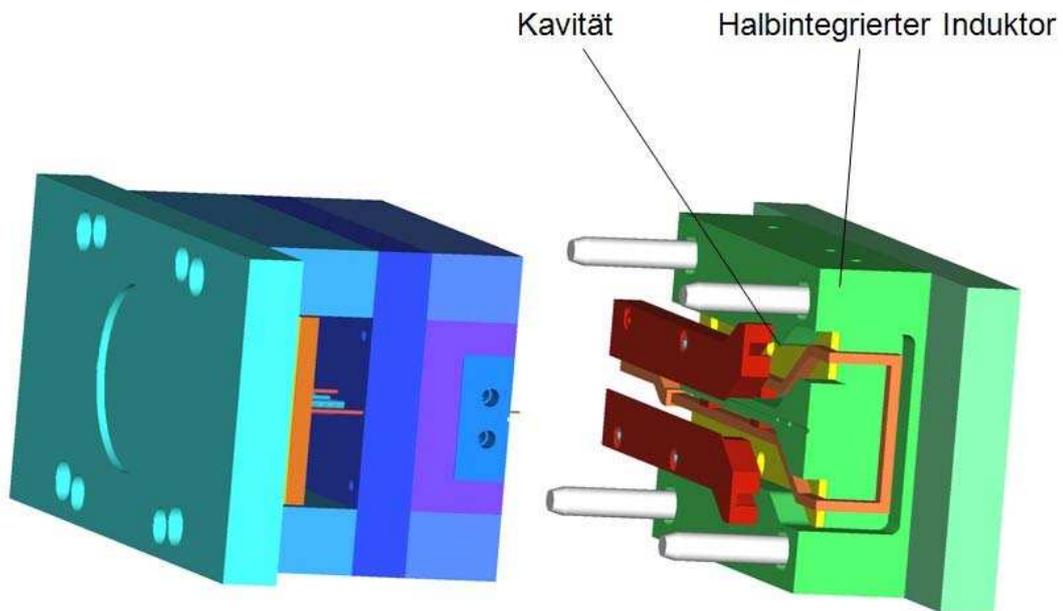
Werkzeug mit halbintegriertem Induktor [1]
